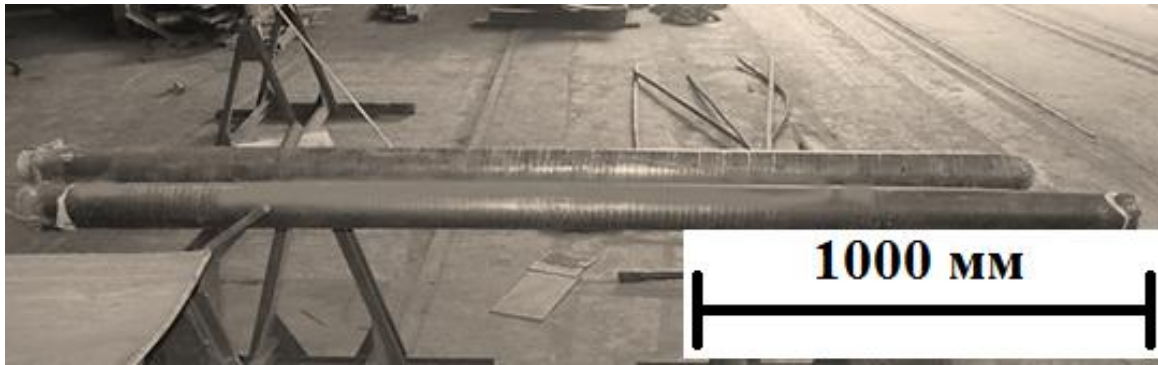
Биметаллические трубные заготовки 37Г2Ф+08Х18Н10Т после сварки взрывом
